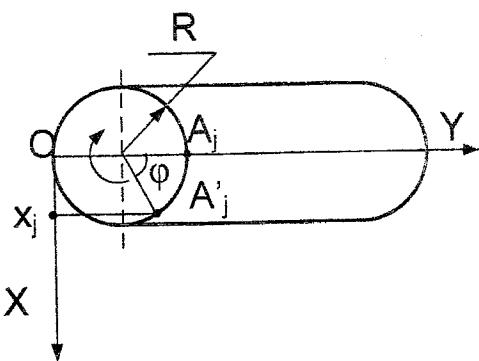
Поворот  $j$ -го лезвия концевой цилиндрической фрезы
